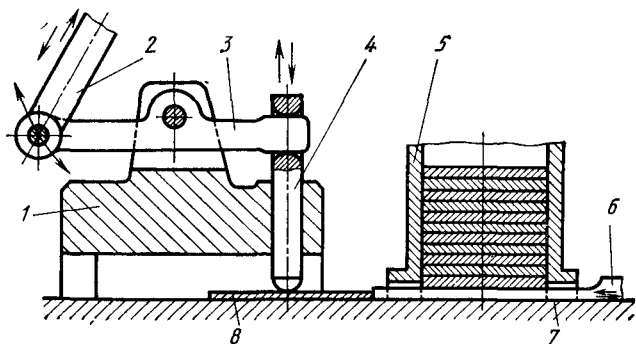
Механический КБУ для контроля толщины заготовки
